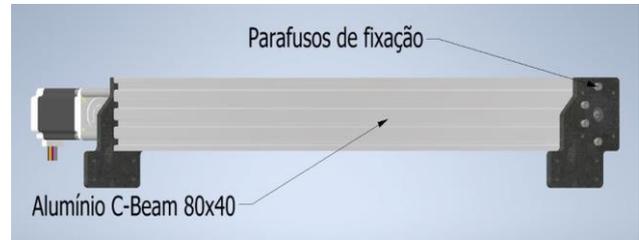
Fixação do perfil estrutural de alumínio a estrutura em aço
